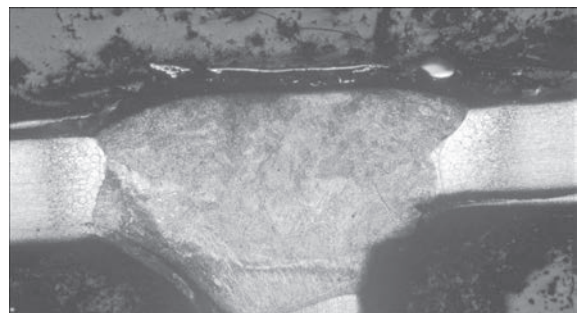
Загальний вигляд таврового зварного з'єднання після ремонтного зварювання ($\times 25$)
